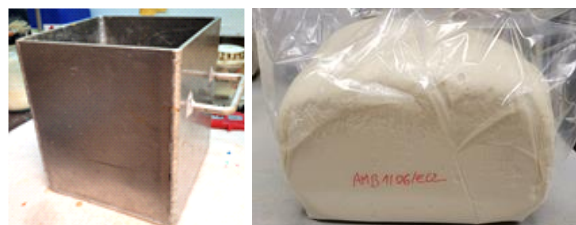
Molde de fabricación a expansión libre (izq.) y ejemplo de probeta obtenida (der.).
